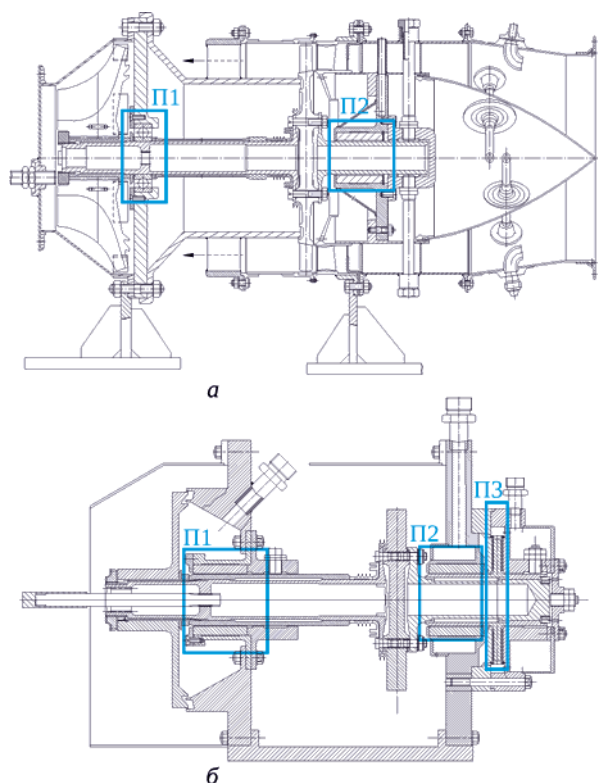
Установка ротора-имитатора с газовыми подшипниками:
